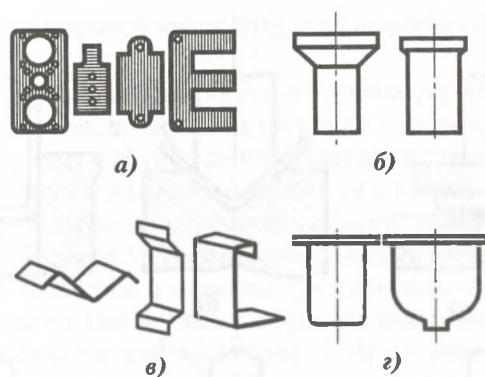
Листовые штампованные детали, полученные вырубкой и пробивкой (а); отбортовкой (б); гибкой (в); вытяжкой и формовкой (г)
